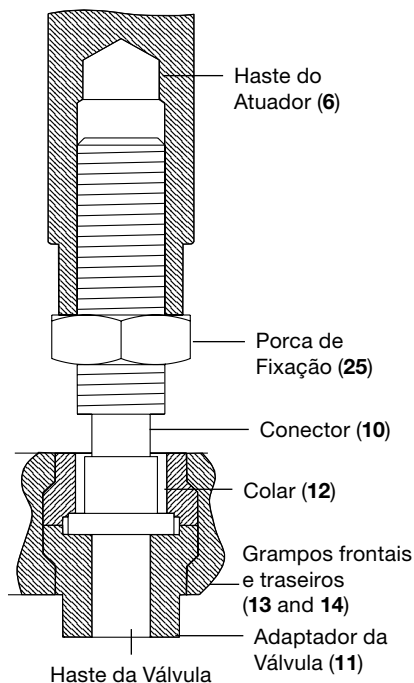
Conjunto de adaptador, adaptador de válvula e conectores
